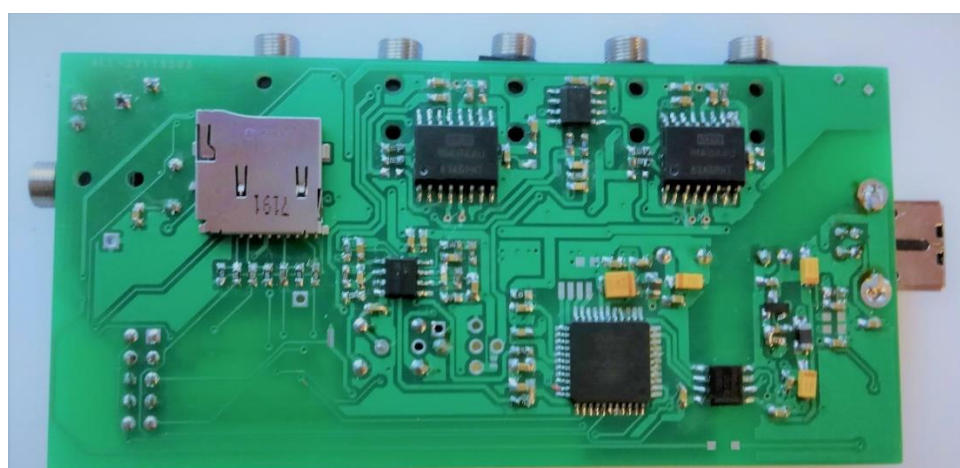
Płytki PCB urządzenia – część górna
